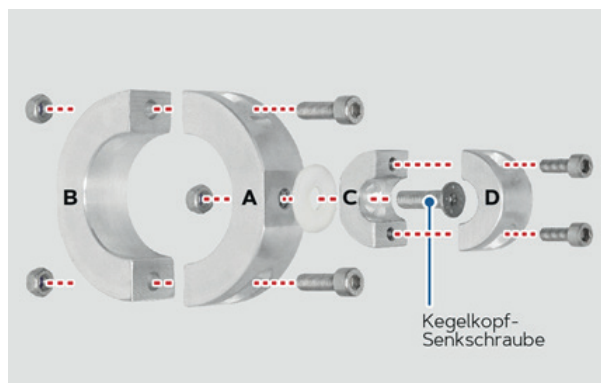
Klemmringhälfte A mit 3 Durchgangsbohrungen. Mittlere Durchgangsbohrung mit Innengewinde. Klemmringhälfte B mit 2 Durchgangsbohrungen. Ringschraube vorne im Bild.
